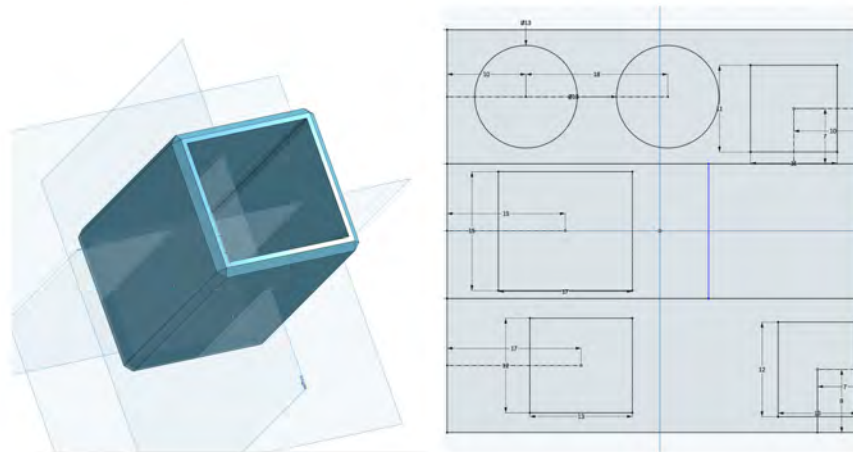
CAD Zeichnung des Gehäuses links 3D- Ansicht des gesamten Gehäuses. Rechts Aufsicht der Frontplatte.
